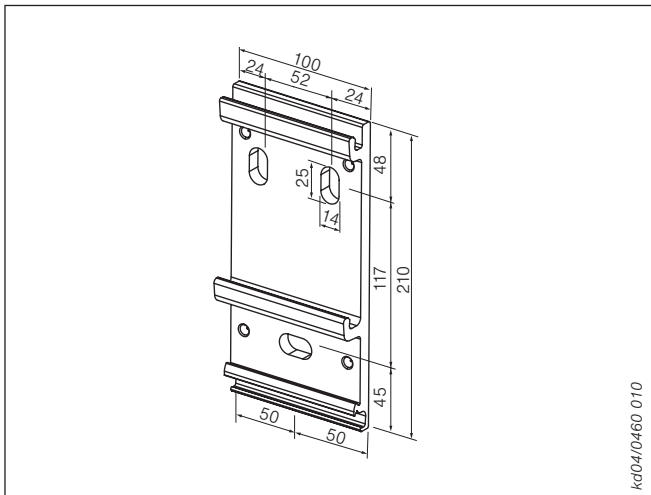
Consola tipo B – Fijación mural con 3 taladros
